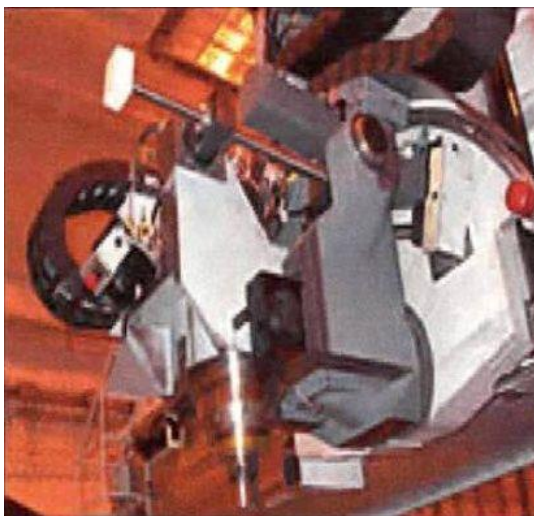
Загальний вид шпindelної головки, що реалізує кути нахилу A, Y шляхом застосування кульково-гвинтових передач фірми Cincinnati Machine Ltd.
